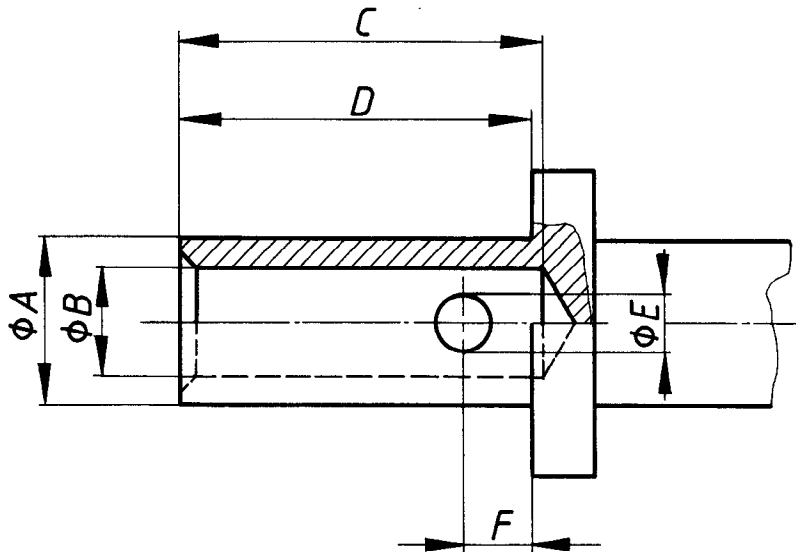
Dimensions de la partie arrière des contacts à sertir
